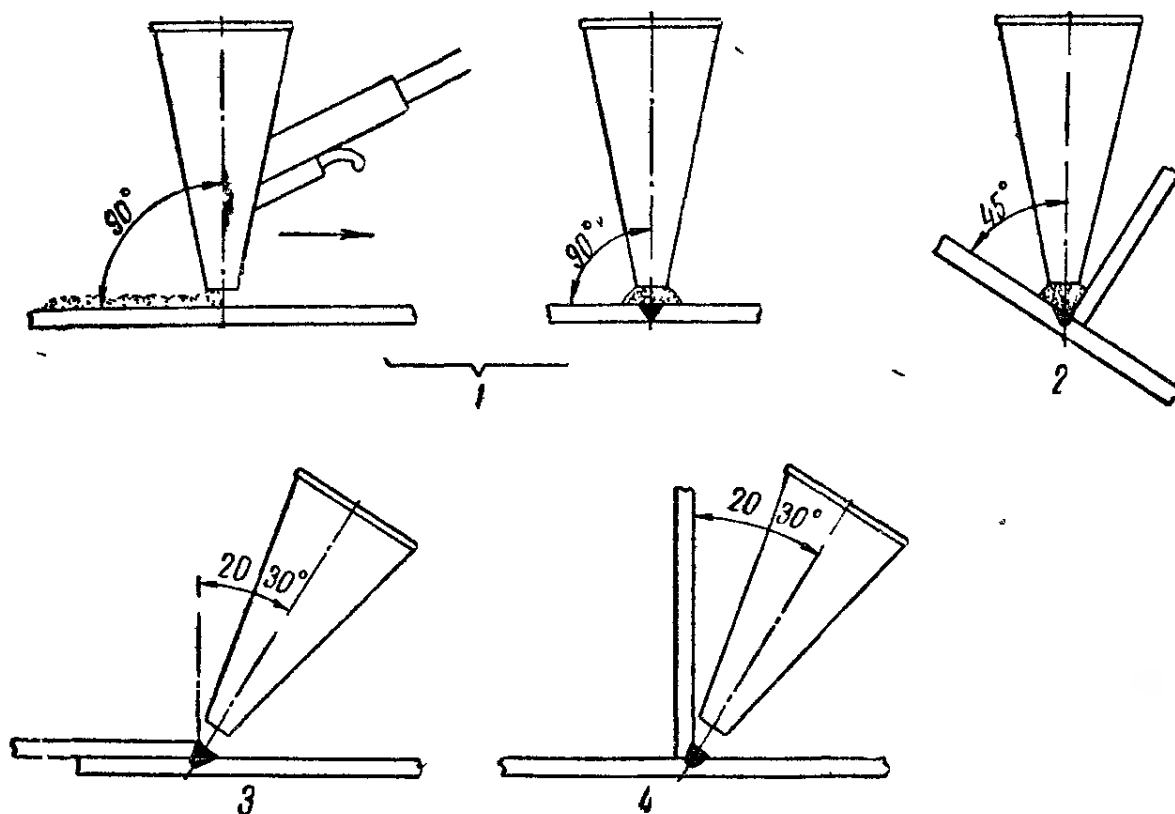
Положение держателя во время шлаговой сварки:
